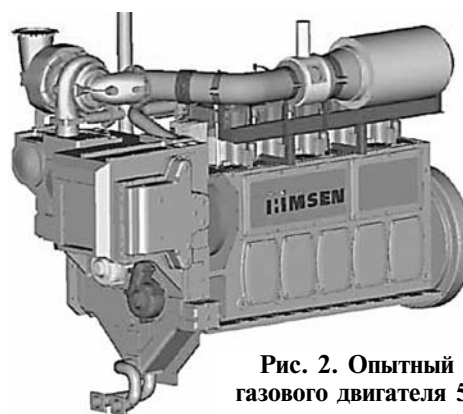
Опытный образец газового двигателя 5Н17/24G
